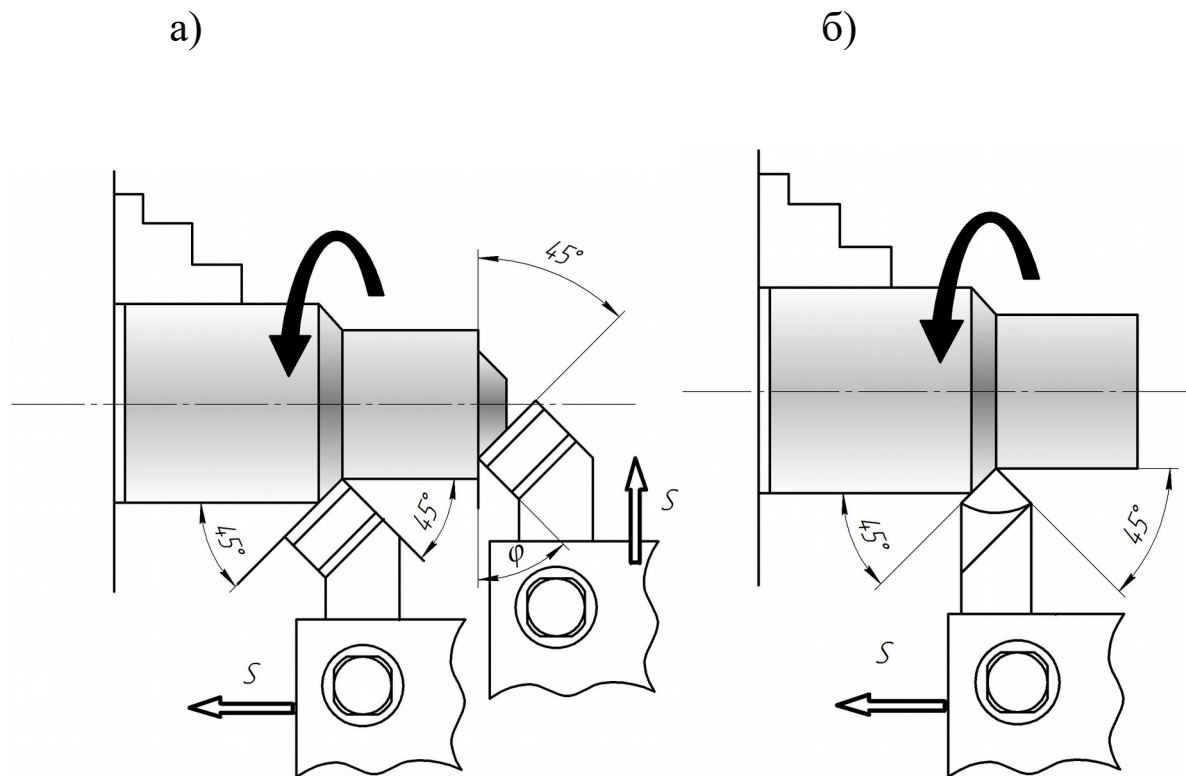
Типи токарних різців та схеми обробки поверхонь
